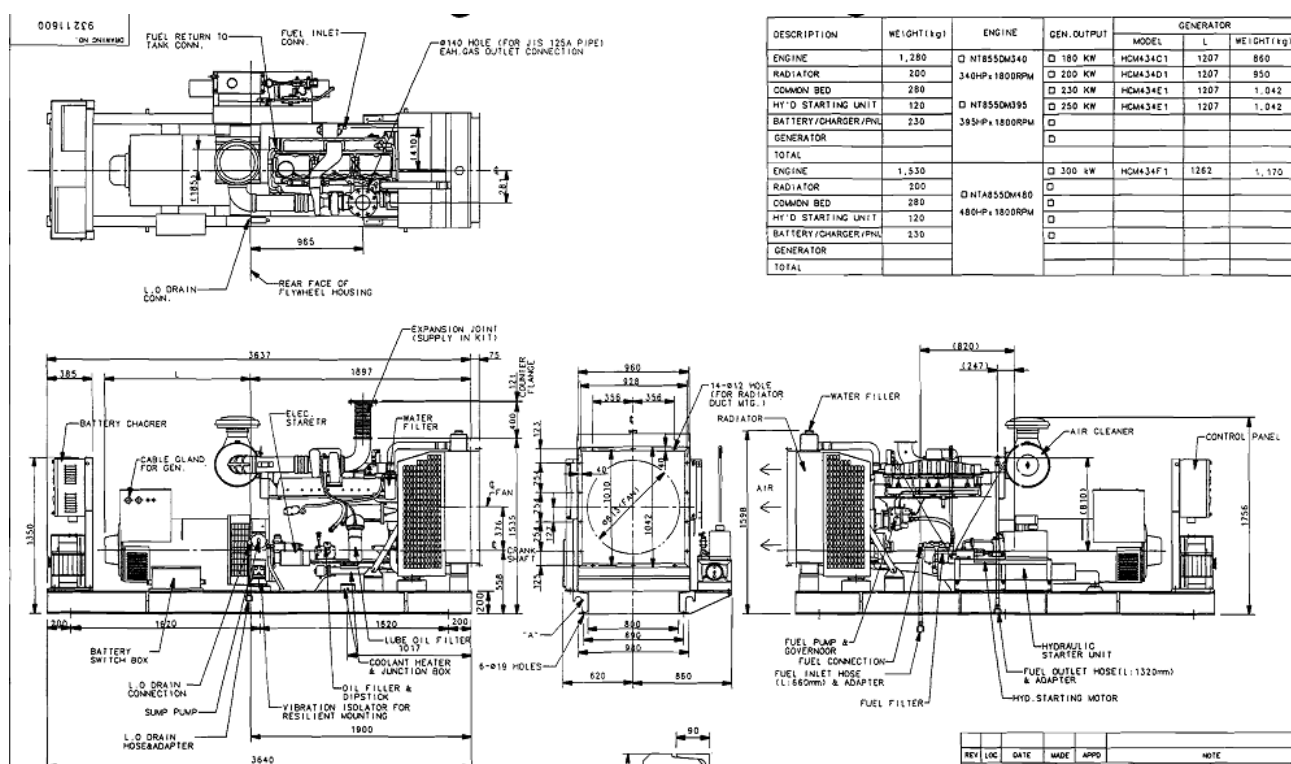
Загальний вид, та габаритні розміри аварійного дизель-генератору
